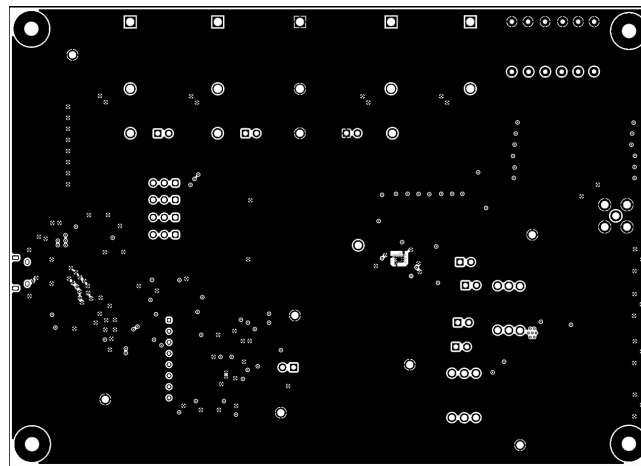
AMC8V208EVM PCB 中层 4 布局 (接地平面)
